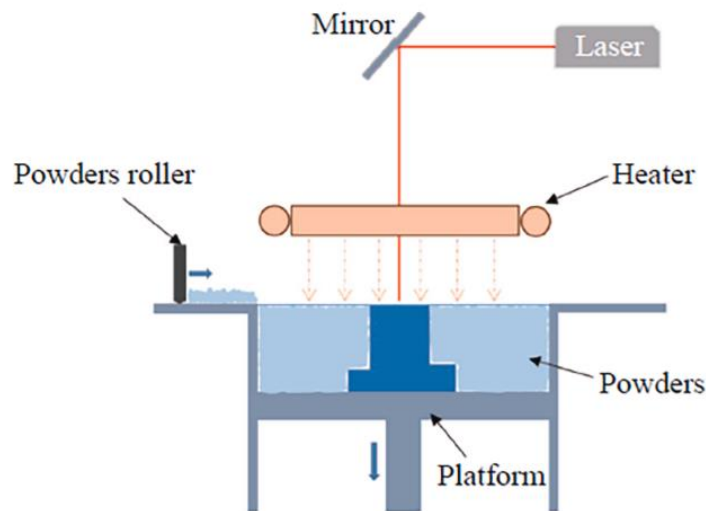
Schéma de principe du procédé Selective Laser Sintering [6].
